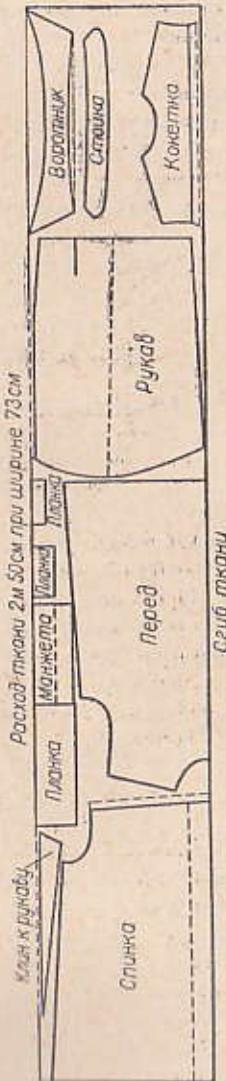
Раскладка на ткани выкройки верхней рубашки.
